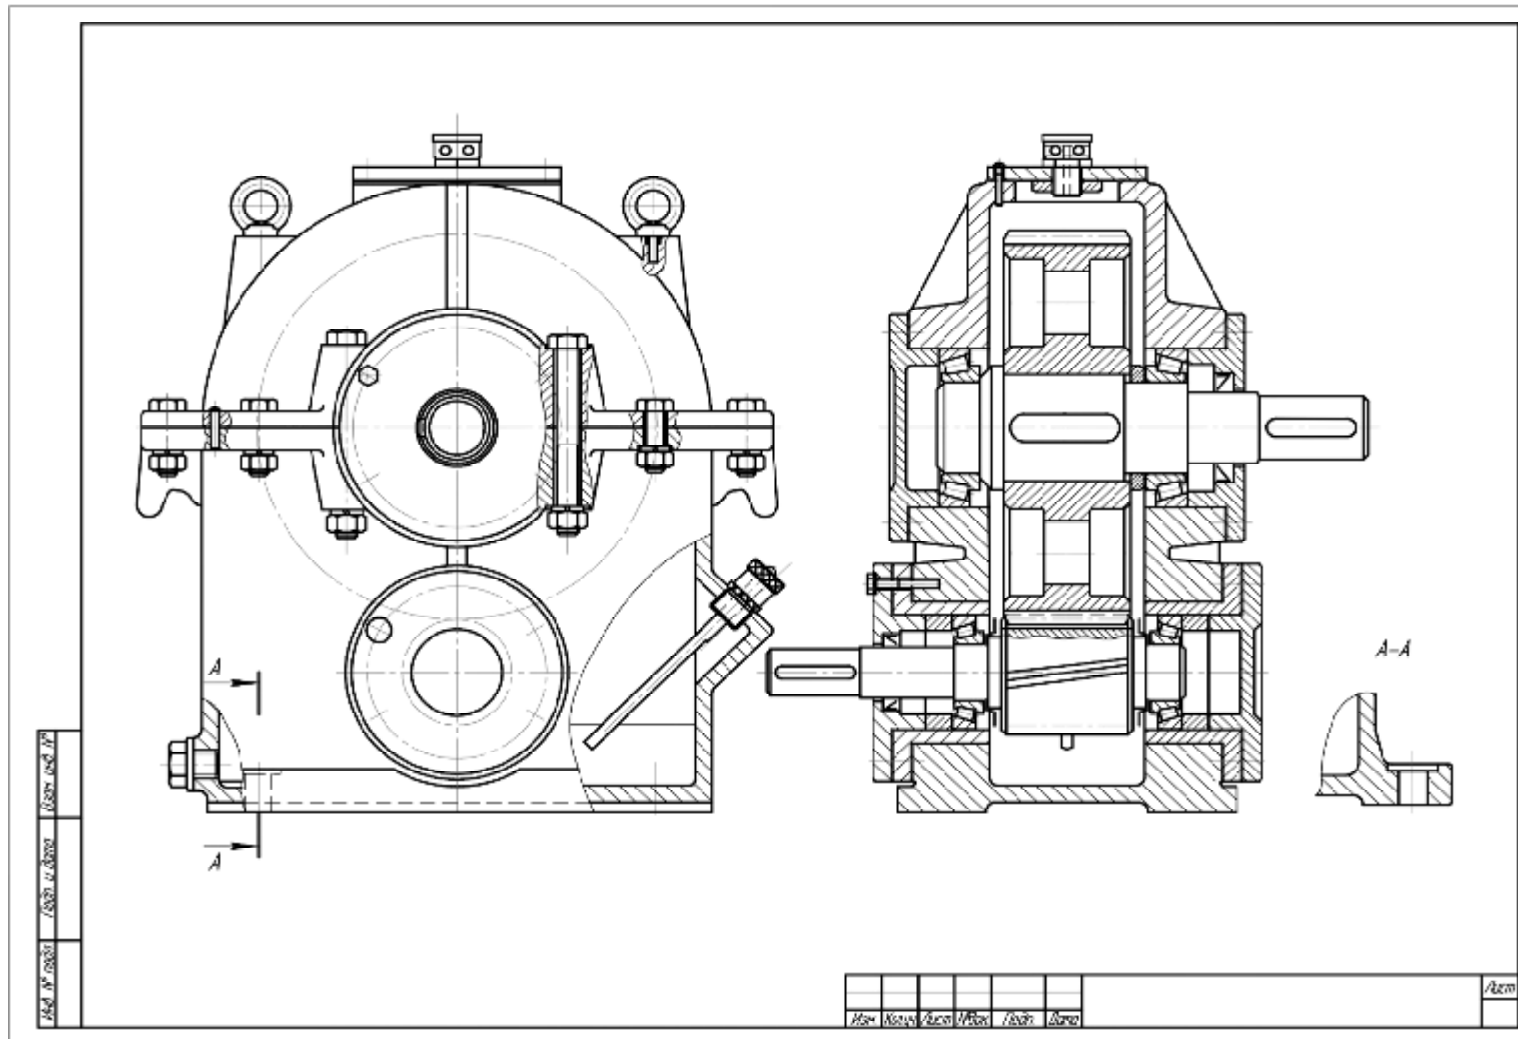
Редуктор цилиндрический одноступенчатый с нижним расположением шестерни
